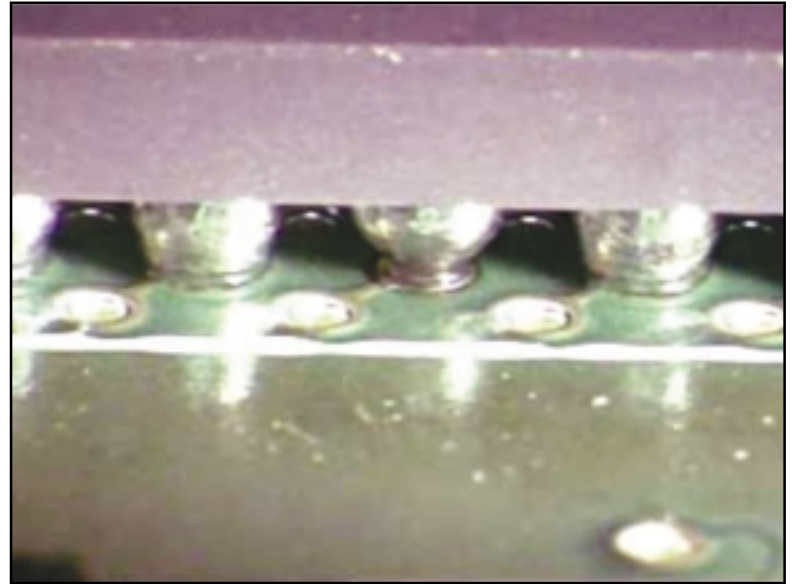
Unión de soldadura abierta en un BGA de plástico eutéctico.
